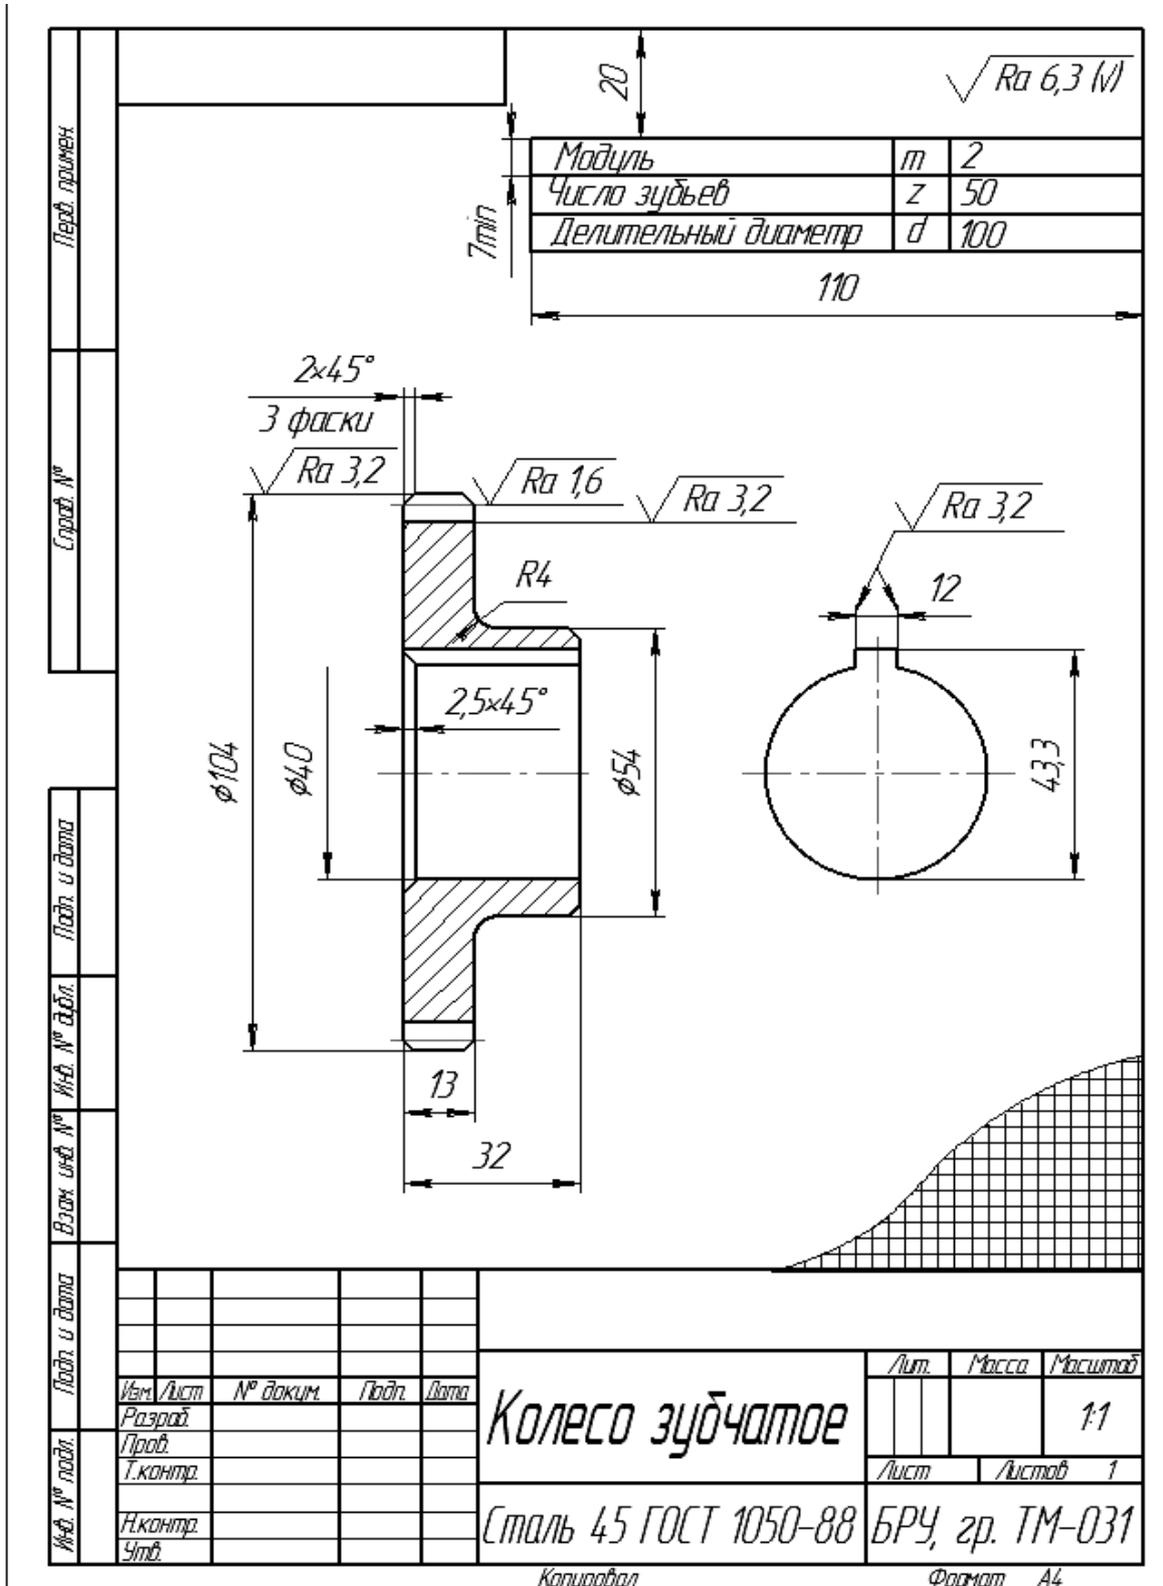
Образец выполнения эскиза колеса зубчатого
